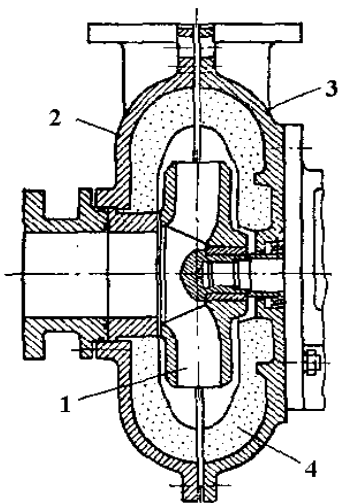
Однокорпусний ґрунтовий насос:
